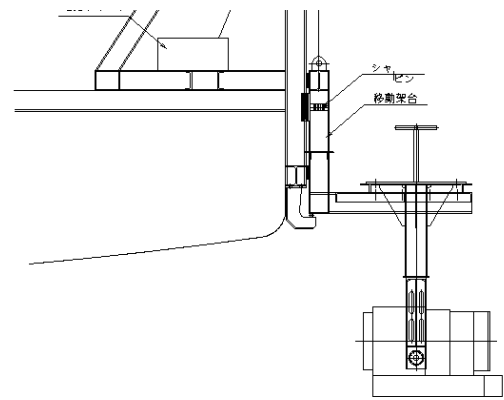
海上試験時の取付ジグの船舶への設置状況
